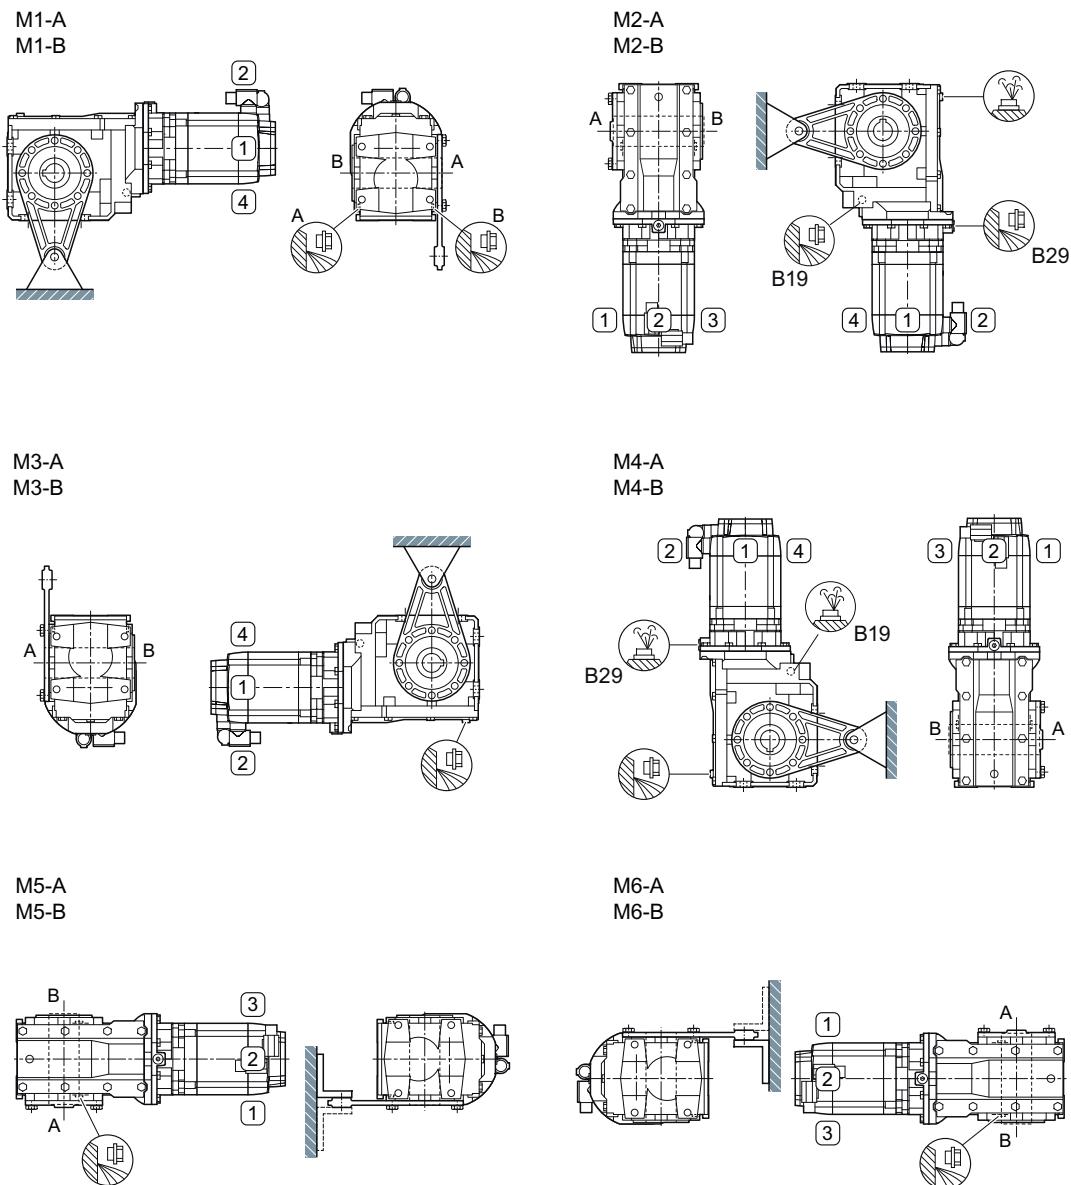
Einbaulagen für Servo-Kegelradgetriebemotor BAD, Aufsteckausführung, Baugrößen 19 - 29, 2-stufig
